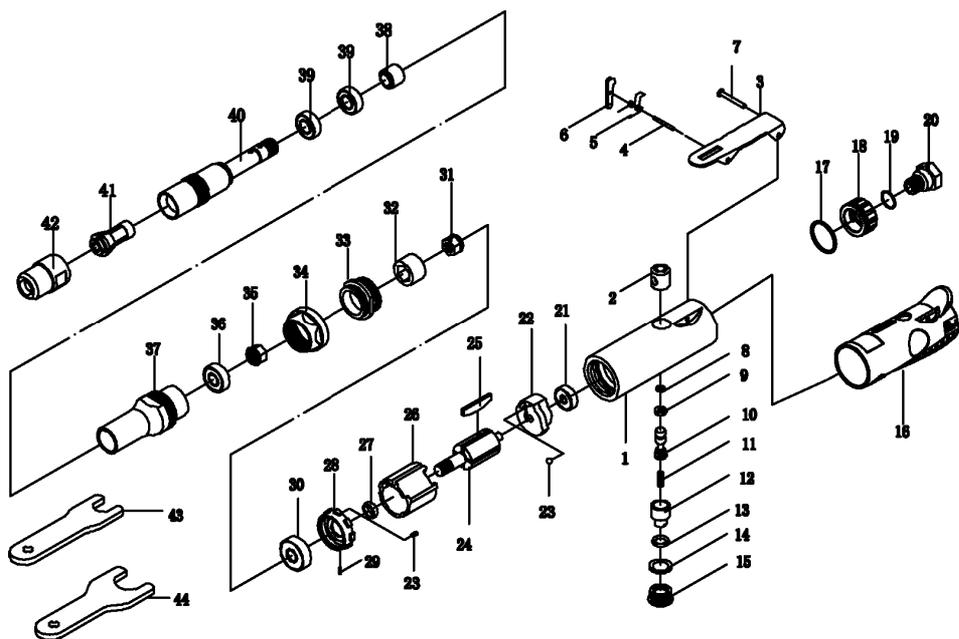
Схема устройства и сборки бормашины ручной пневматической MFG-222/000-2
